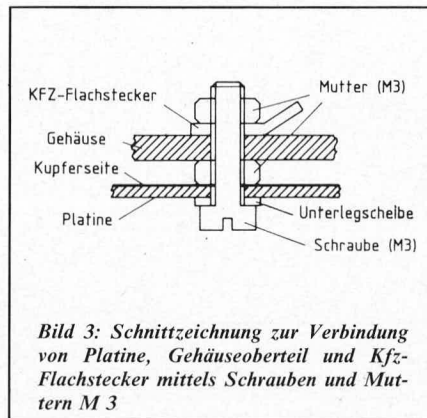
Schnittzeichnung zur Verbindung von Platine, Gehäuseoberteil und Kfz-Flachstecker mittels Schrauben und Muttern M 3
